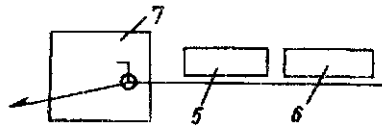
Структура условного обозначения нестандартного сварного шва: 5-7 — то же, что на рис. 8.3
